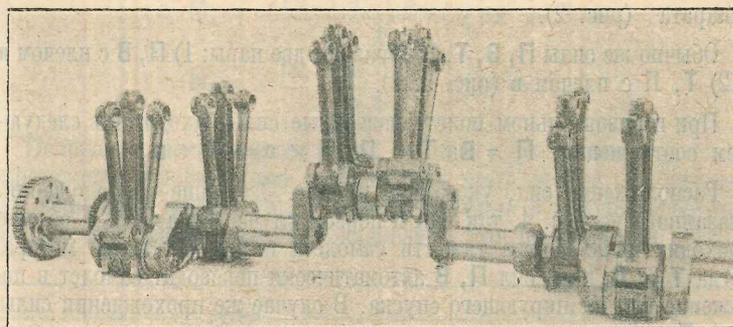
Коленчатый вал 18-ти цилиндрового авиационного двигателя Фармана в 600 л. с.
